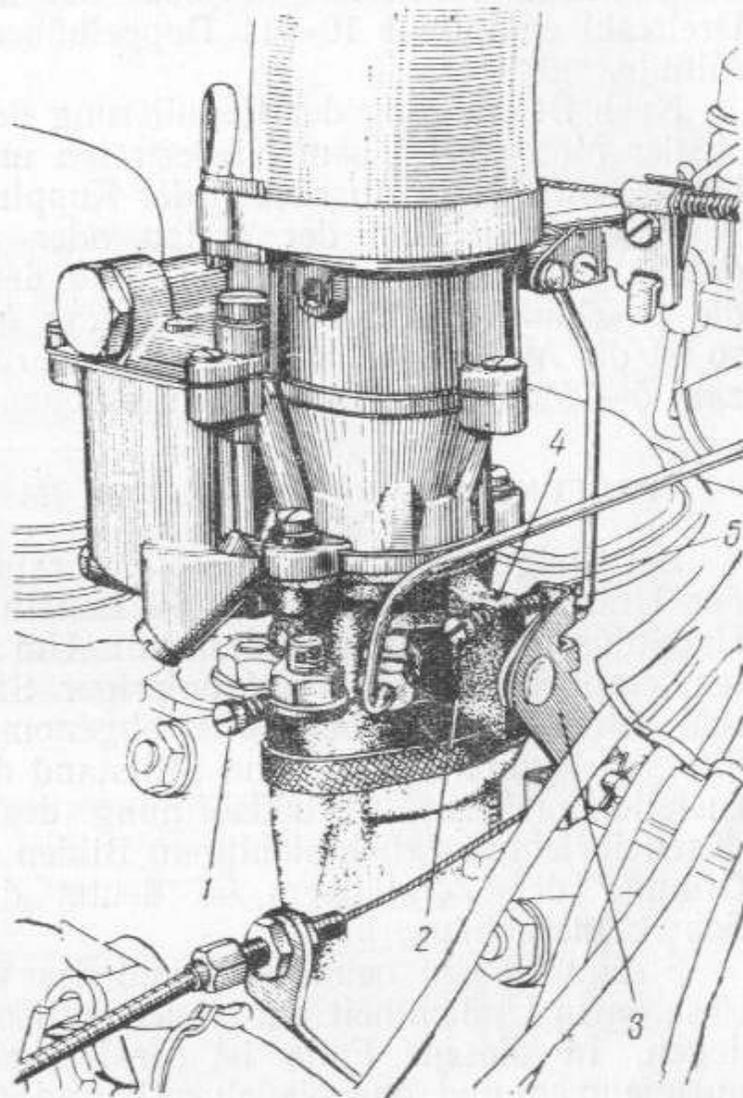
Regulierschrauben des Vergasers für Gemischbildung beim Leerlauf
